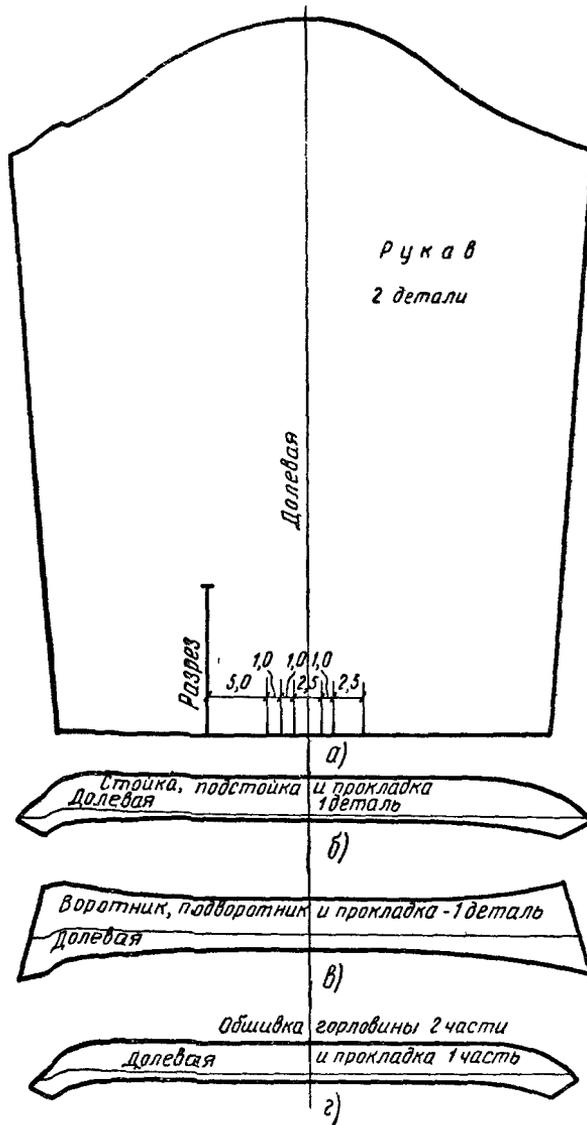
Детали кроя а) рукав, б) стойка, в) воротник, г) обшивка
